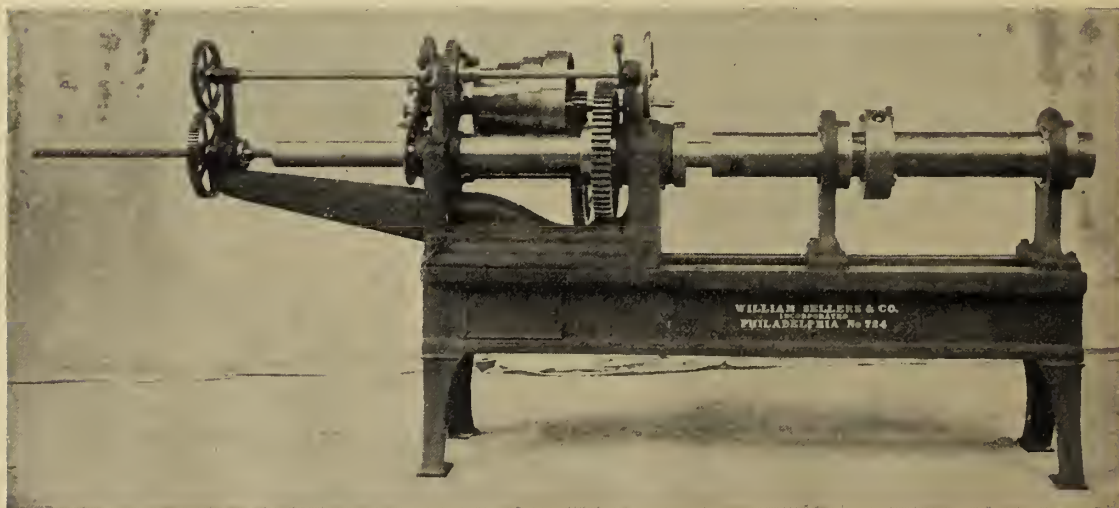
Machine à aléser les coussinets de locomotives types *Sellers*.
